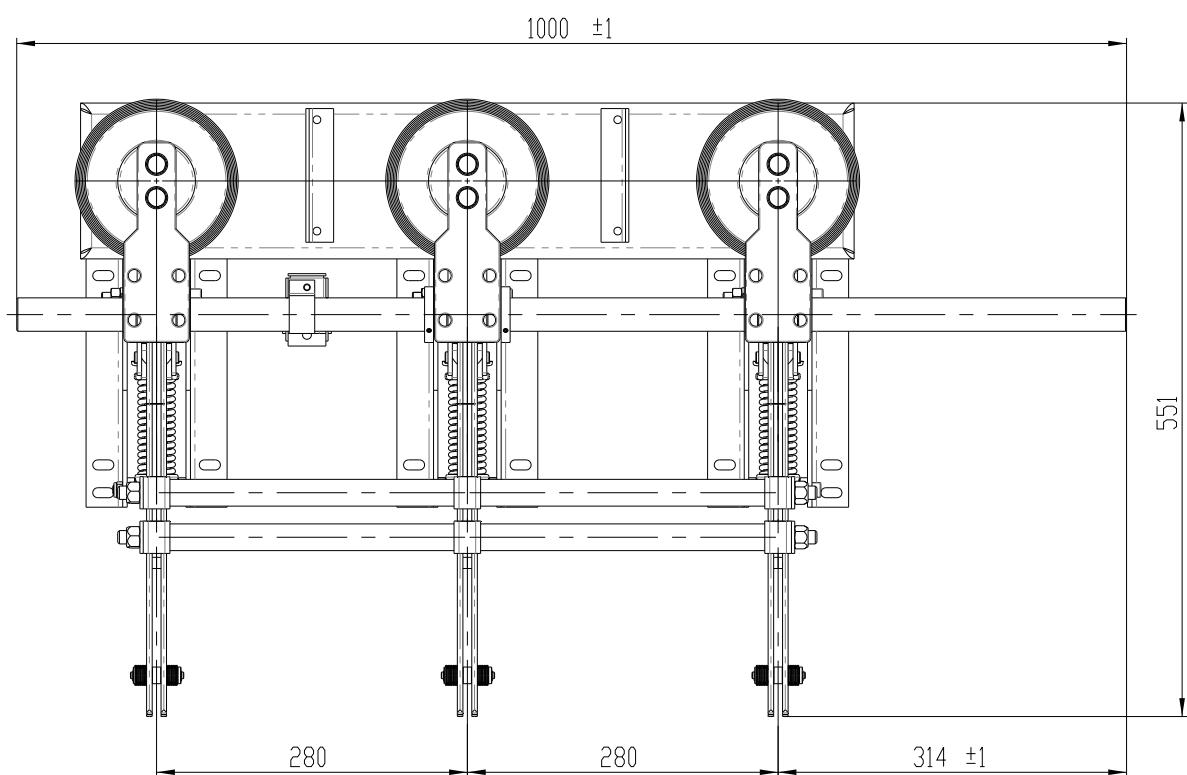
Габаритные, установочные и присоединительные размеры заземлителя с номинальным напряжением 35 кВ с межфазным расстоянием 280 мм
